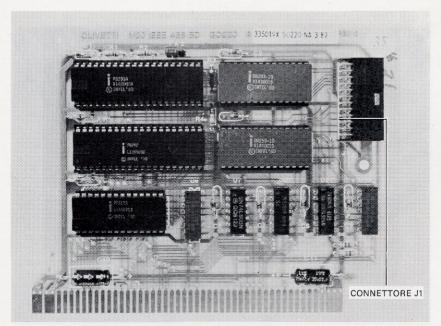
Piastra IEEE 488 - Posizione del connettore
